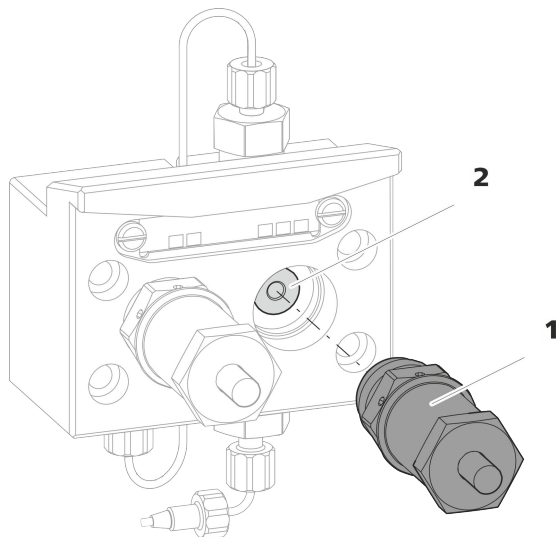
Desmontaje de cabezal de bomba – cartucho de pistón
